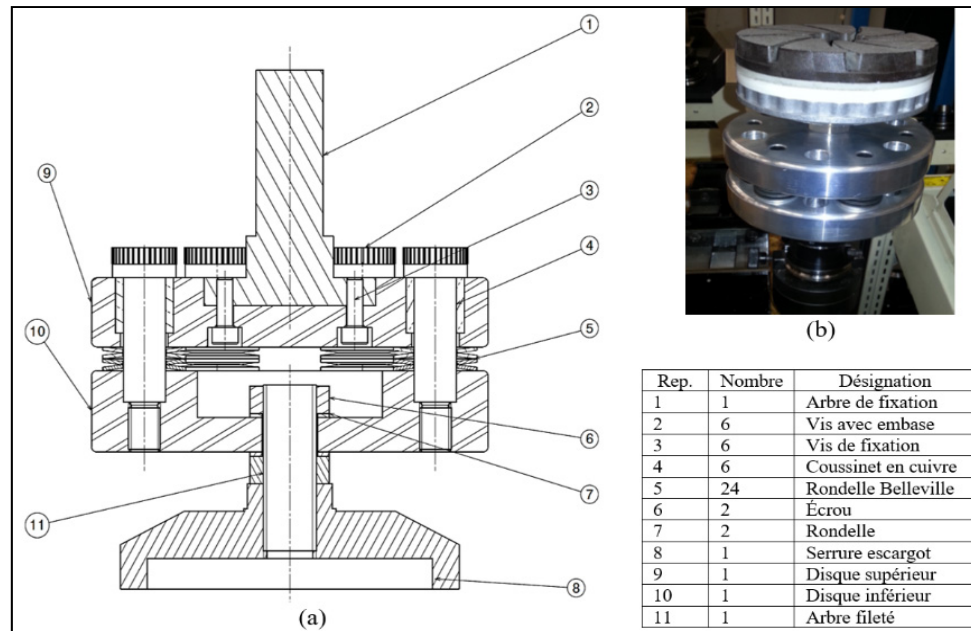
Outil de polissage : (a) Dessin d'ensemble du porte-outil
